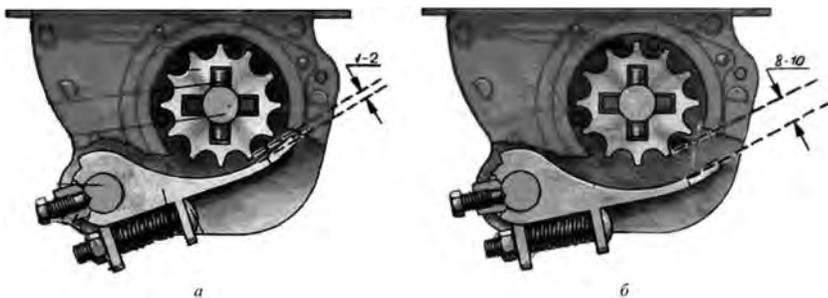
Регулировка положения клапана катушечного высевающего аппарата:
